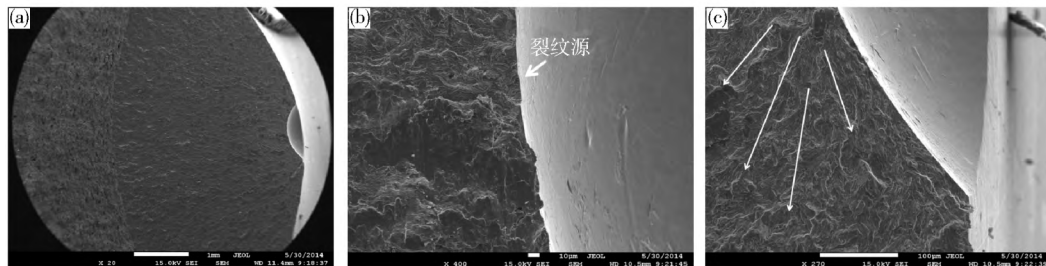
压痕试样典型断口形貌。(a) 断口形貌; (b) 压痕底部裂纹萌生点; (c) 压痕附近裂纹扩展形貌
